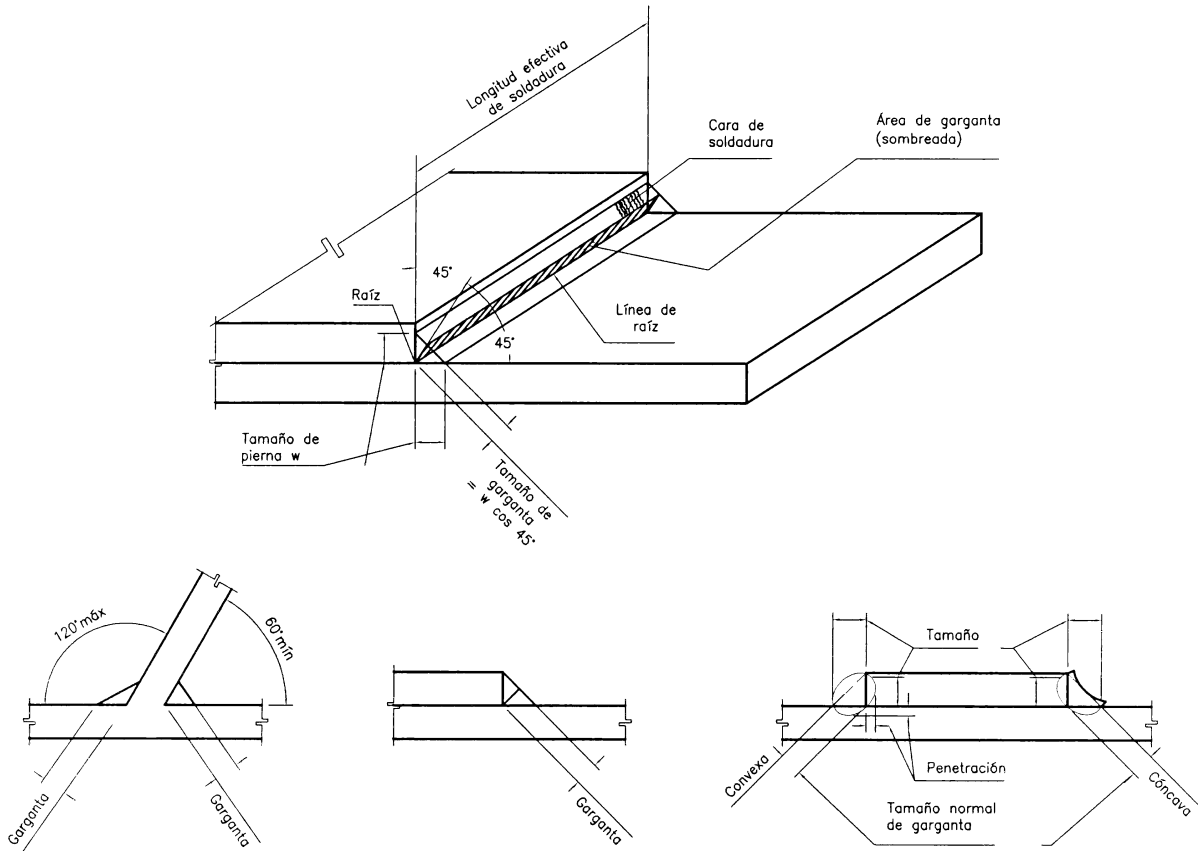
Nomenclatura de soldadura de filete
